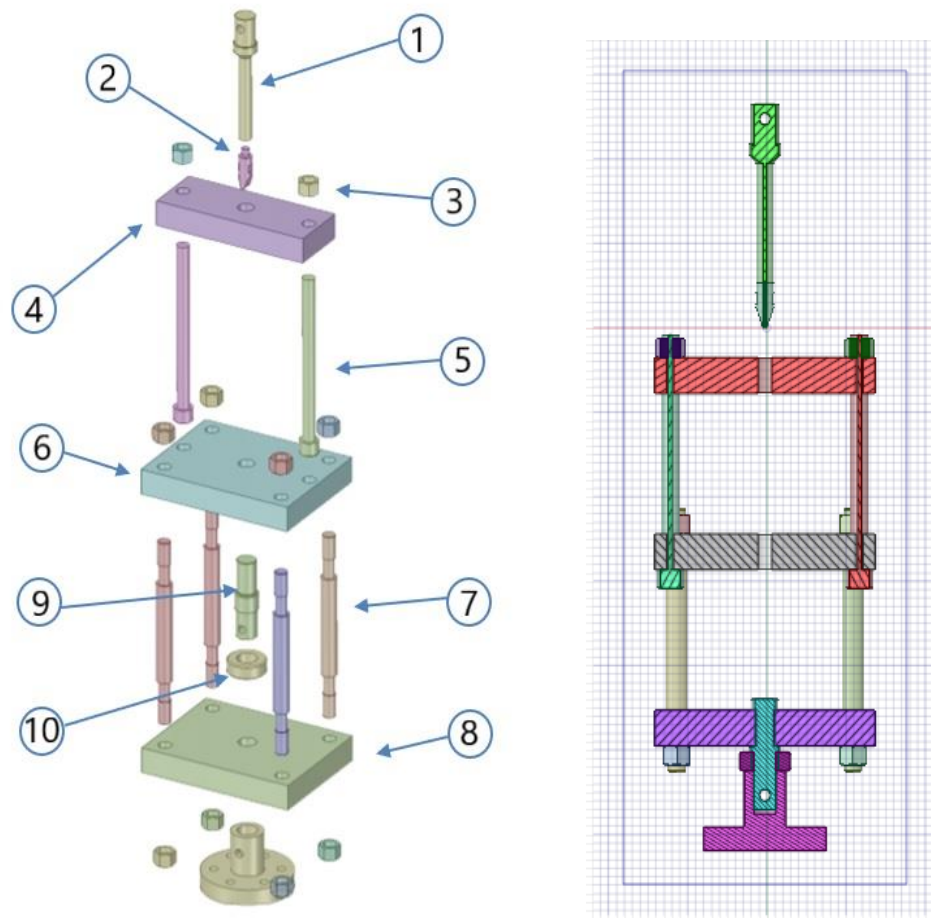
Vista explodida do dispositivo de perfuração / Vista em corte do dispositivo
